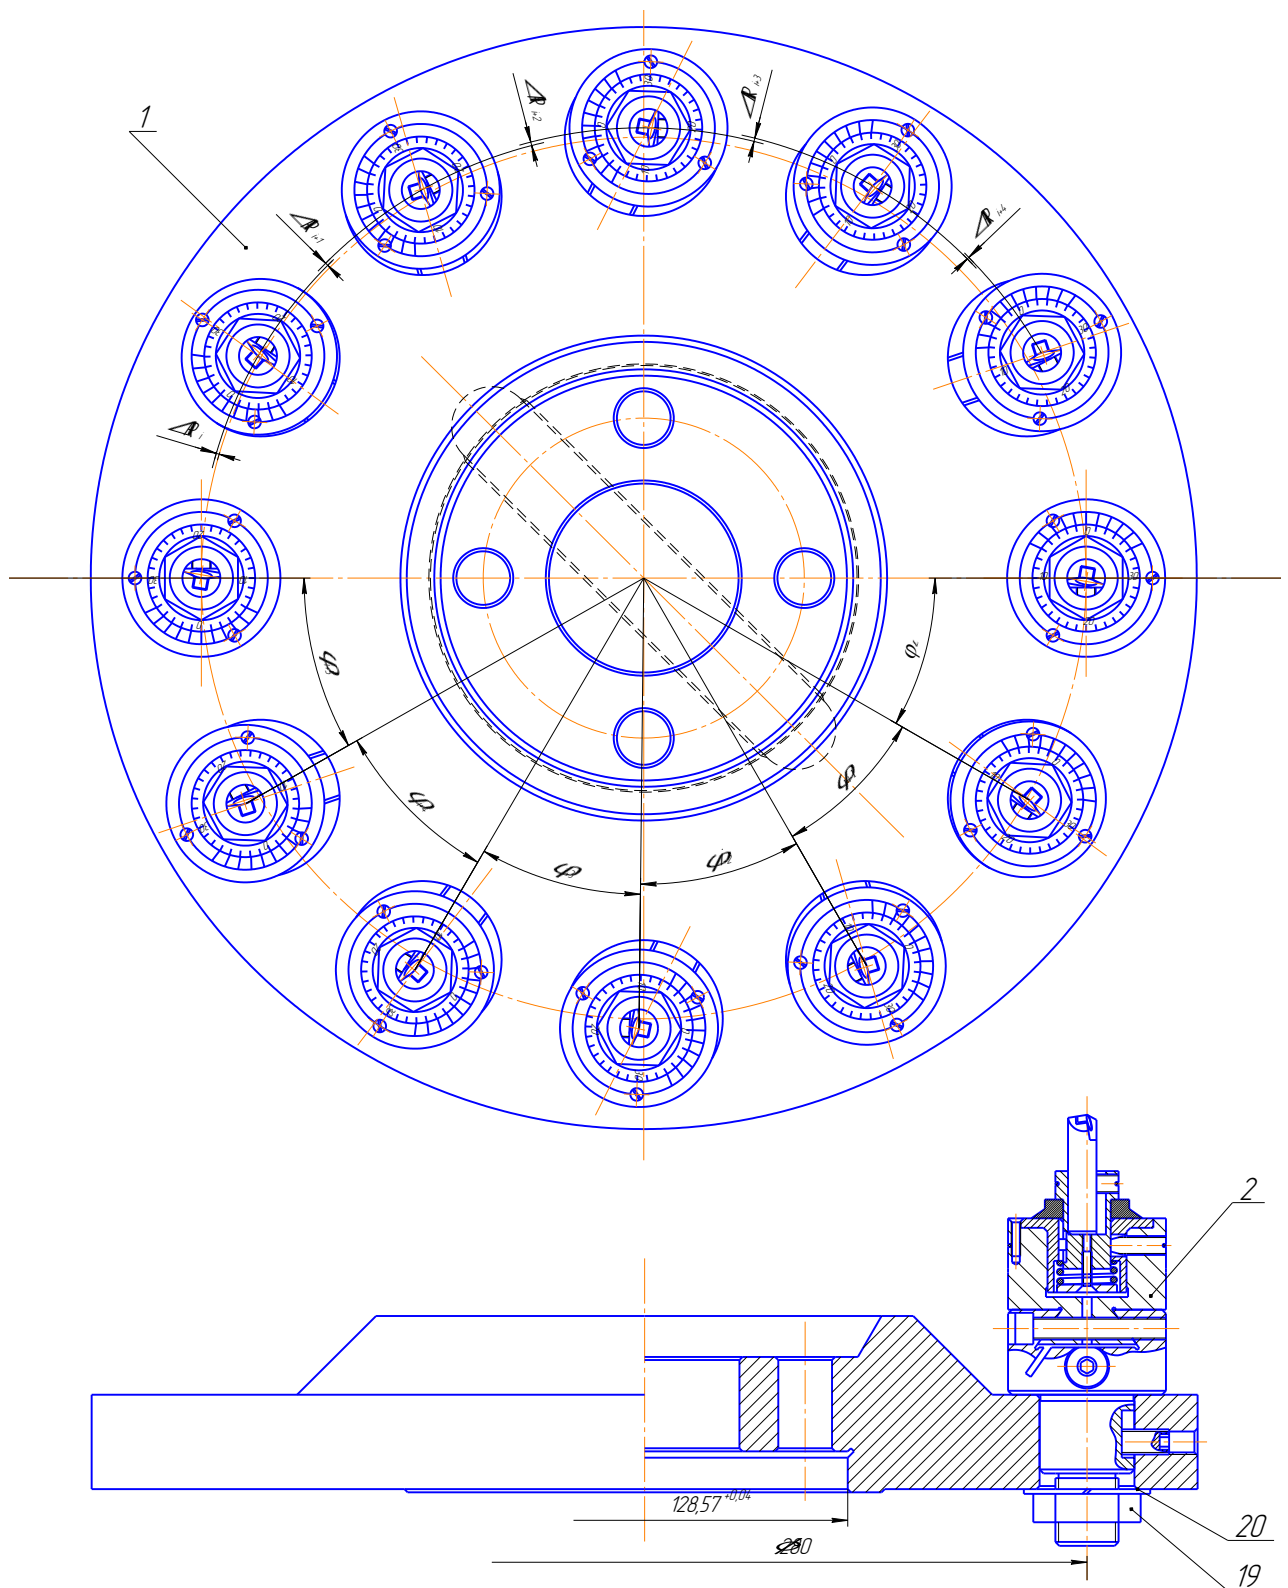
Конструкція фрези для глибинної обробки плоских поверхонь
